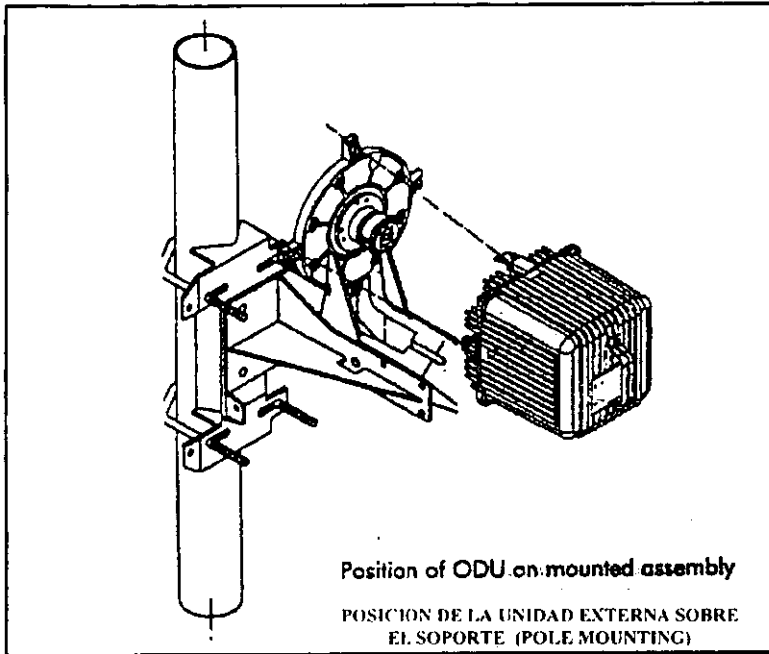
e) - Instalación del equipo de radio sobre el pole mounting (soporte)
